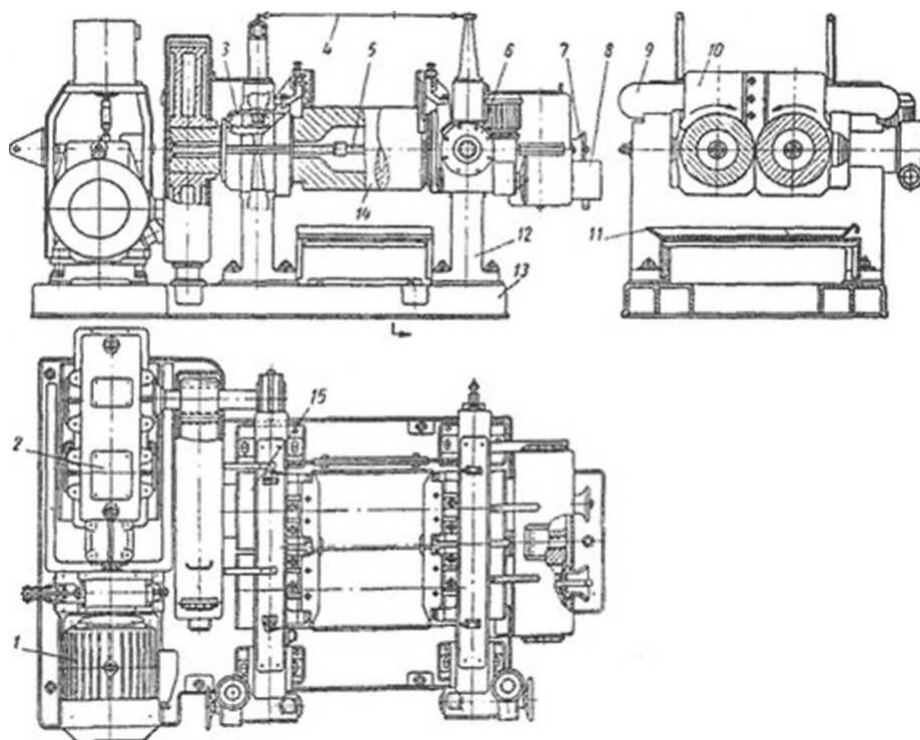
Общий вид вальцов: 1 - электродвигатель; 2 - редуктор; 3 - подшипники переднего вальца; 4 - аварийное устройство; 5 - охлаждающее устройство; 6 - механизм регулирования зазора; 7 - сливная воронка; 8 - ванна; 9 - траверса; 10 - ограничительные стрелы; 11 - поддон; 12 - станины; 13 - фундаментная плита; 14 - вальцы; 15 - подшипники заднего вальца.
